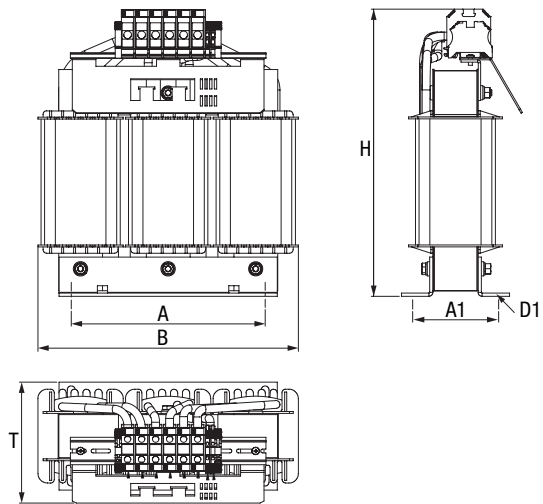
Maßzeichnung Hochsetzdrossel beispielhaft für BG5 und BG6A
